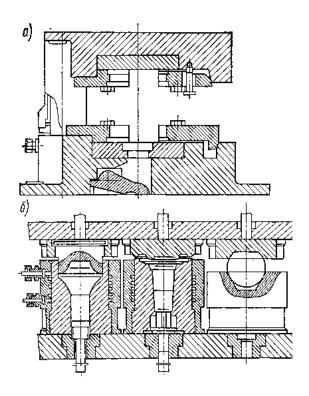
Схема пакета (а) и ручьевые вставки (б) трехручьевого штампа для выдавливания цапфы поворотного кулака
